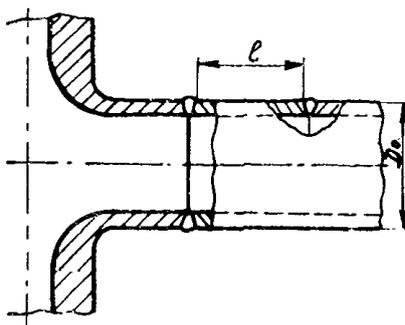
Расположение сварных соединений приварки трубопроводов к патрубку
